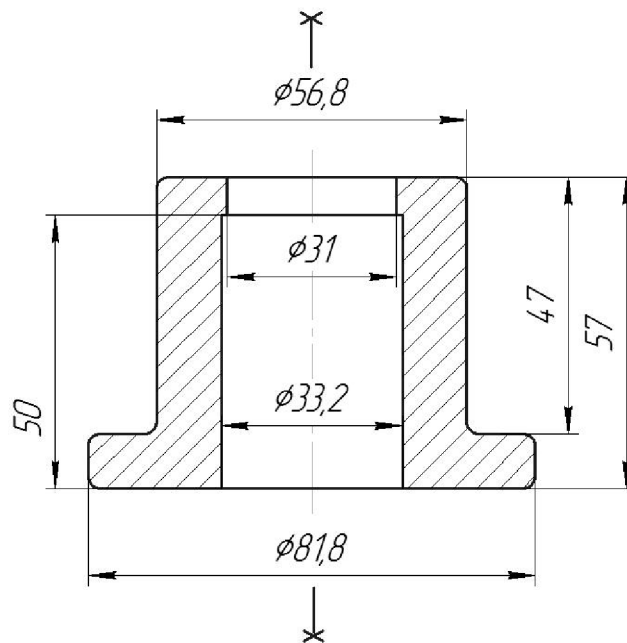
Ескіз заготовки, отриманої литтям в облицьований кокіль
